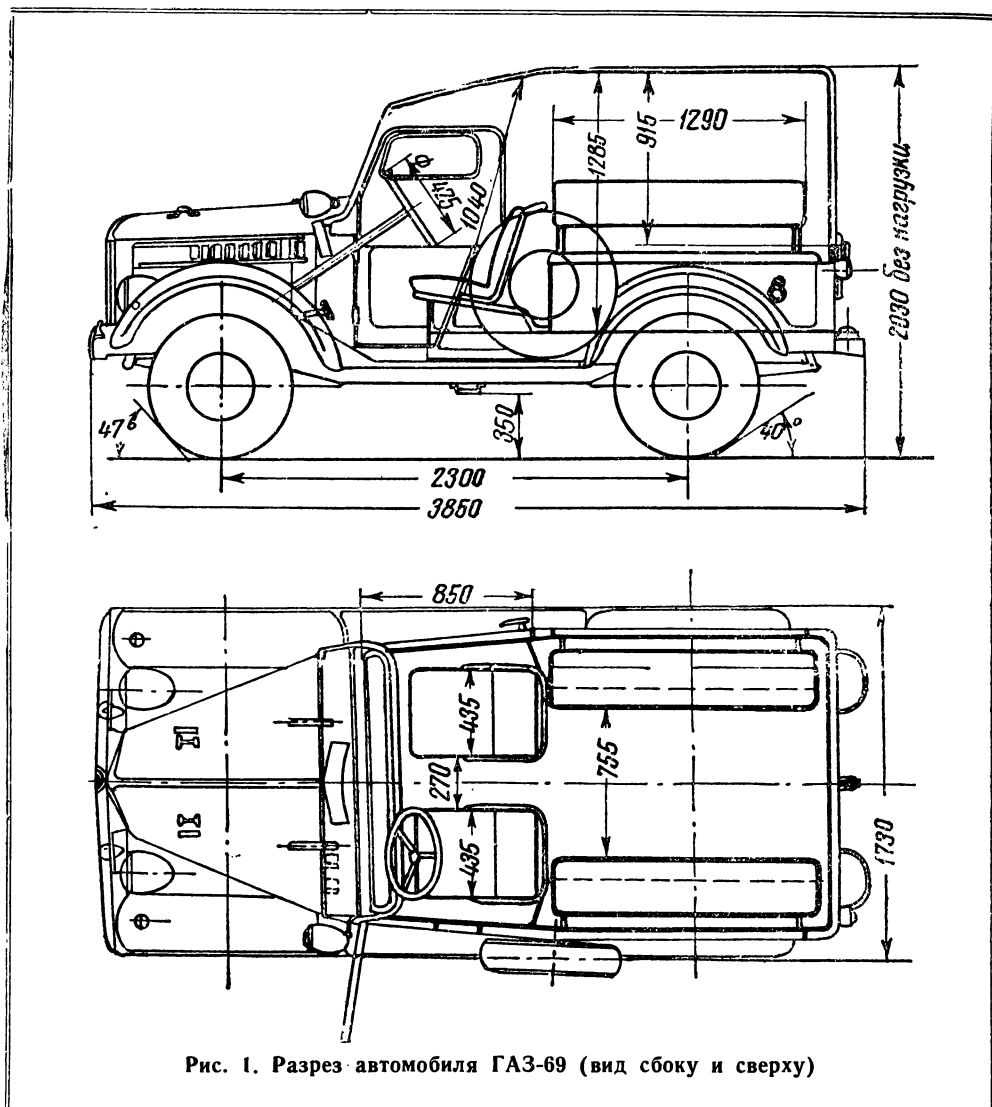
Разрез автомобиля ГАЗ-69 (вид сбоку и сверху)
